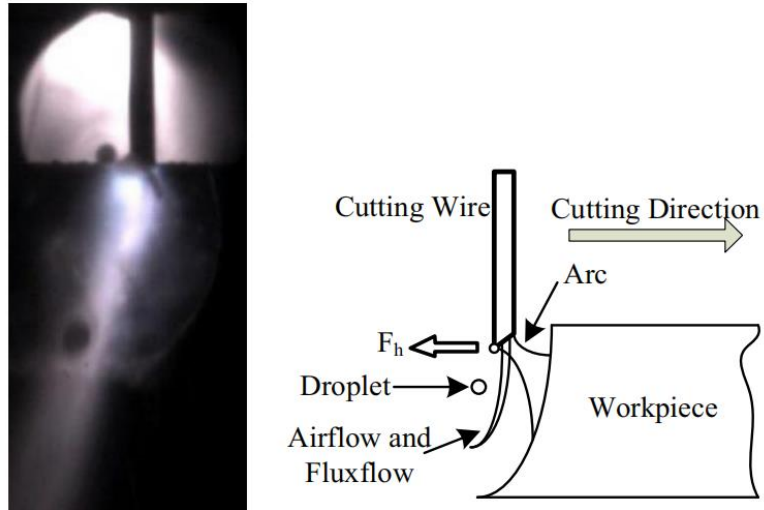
Схема резки стали порошковой проволокой на воздухе [105]
